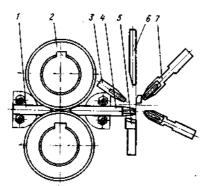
Инструментальный блок автоматов холодной навивки пружин кулисного вида
